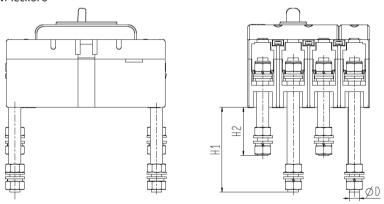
Габаритные размеры заднего присоединения ЗП-300 на выключатели автоматические до 250A
